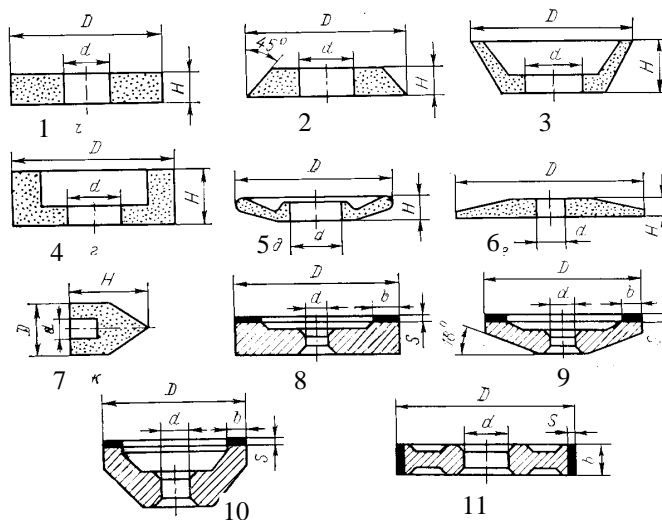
Шлифовальные круги для заточки и доводки дереворежущего инструмента
